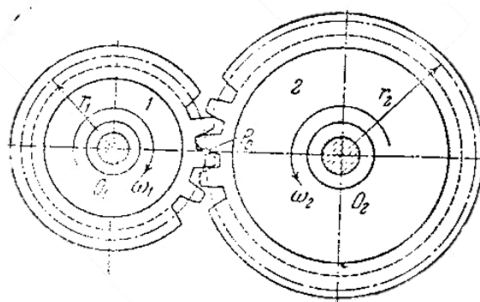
Трёхзвенный зубчатый механизм:
